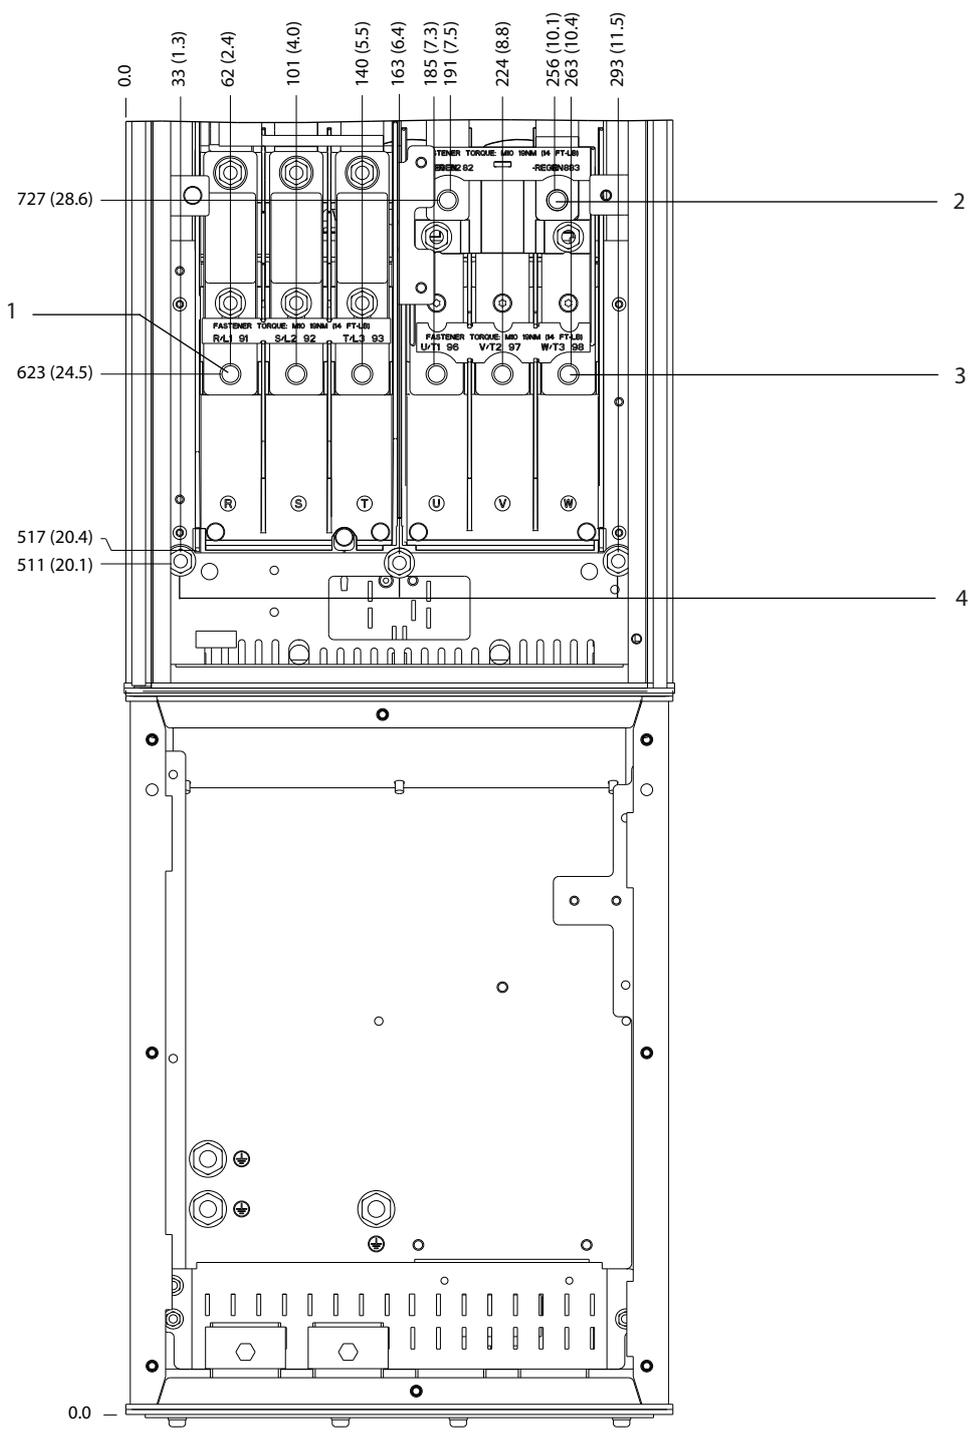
Dimensões do terminal do D5h com opcional de desconexão (vista frontal)
